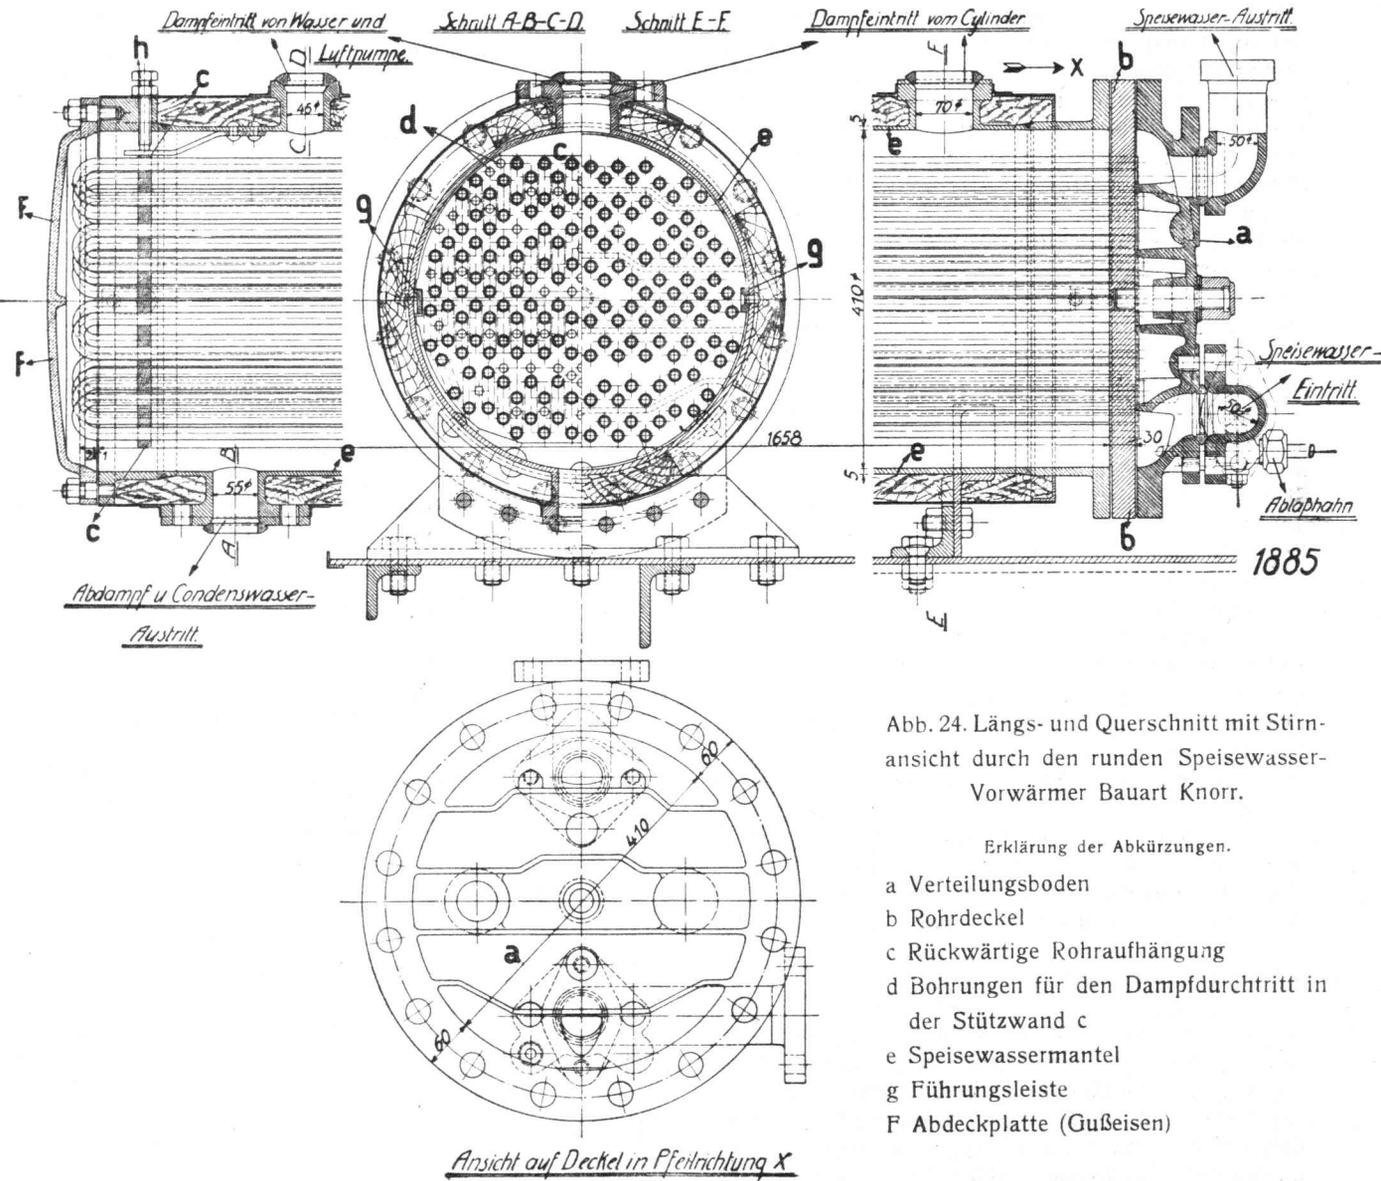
Längs- und Querschnitt mit Stirnansicht durch den runden Speisewasser-Vorwärmer Bauart Knorr.
